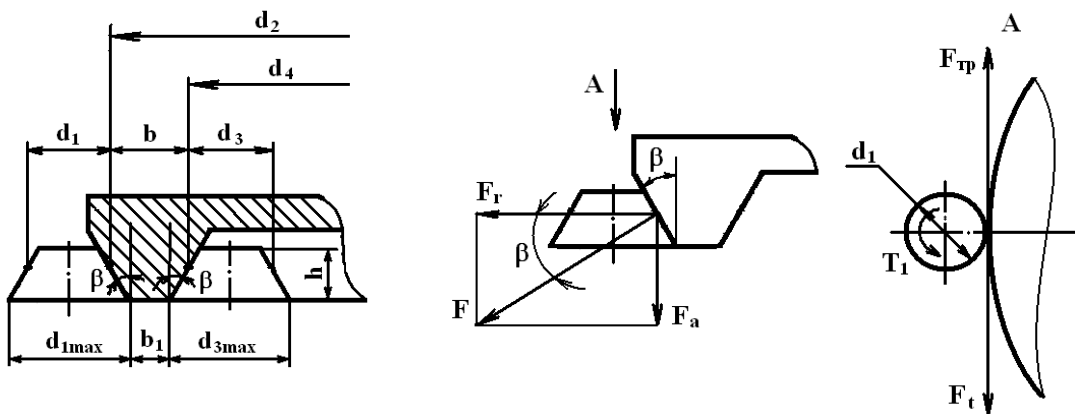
Розрахункова схема фрикційної передачі приводу
